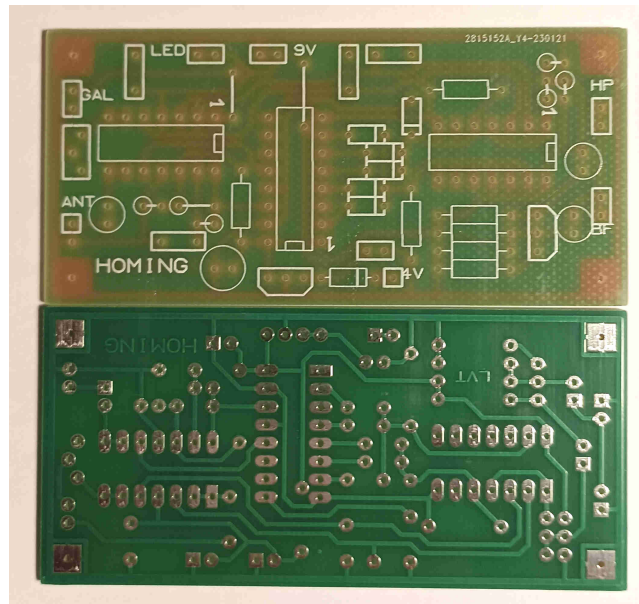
Le circuit imprimé du boîtier « Homing Toutes Bandes », côté composants et côté soudures
